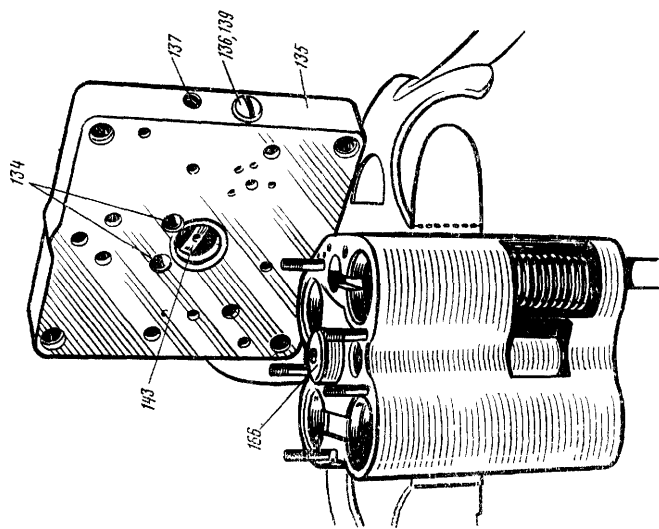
134 — клапаны масляного насоса; 135 — основание; 136 — пробка-заглушка иглы изодрома; 137 — заглушка канала выпуска масла; 139 — игла изодрома; 143 — приводной вал; 162 — корпус узла регулирования; 166 — втулка
